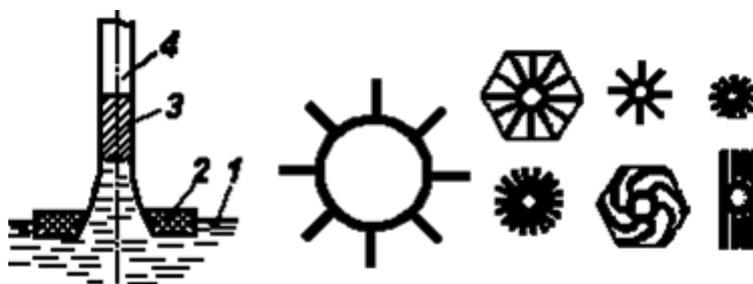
Схема литья намораживанием и примеры сечений отливок:
